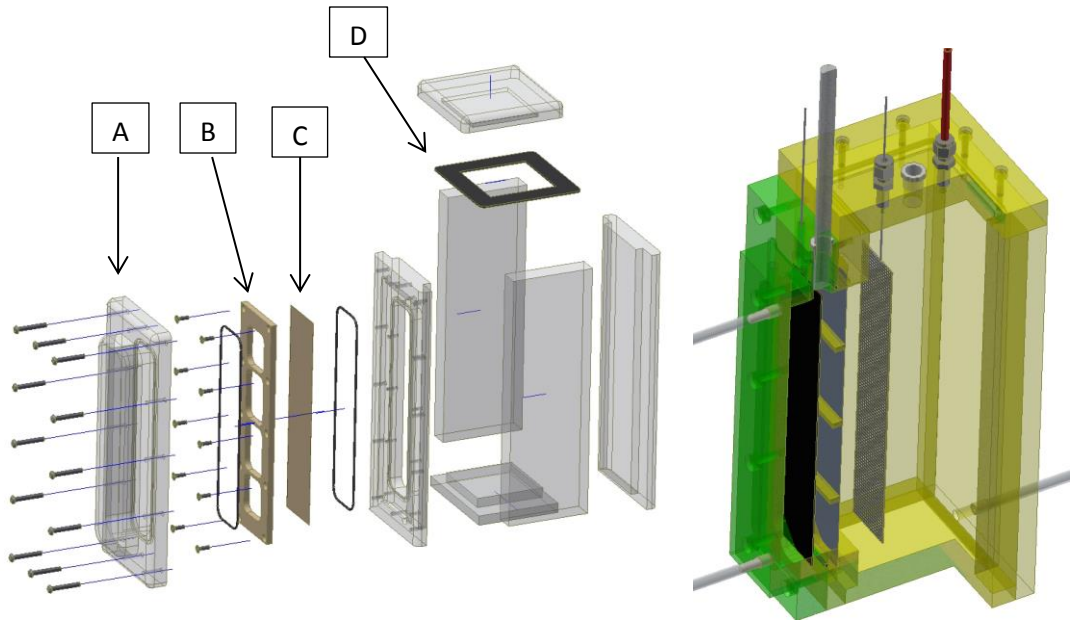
A gauche : Vue éclatée du prototype ; A droite : Prototype en coupe, vue en perspective ¾
